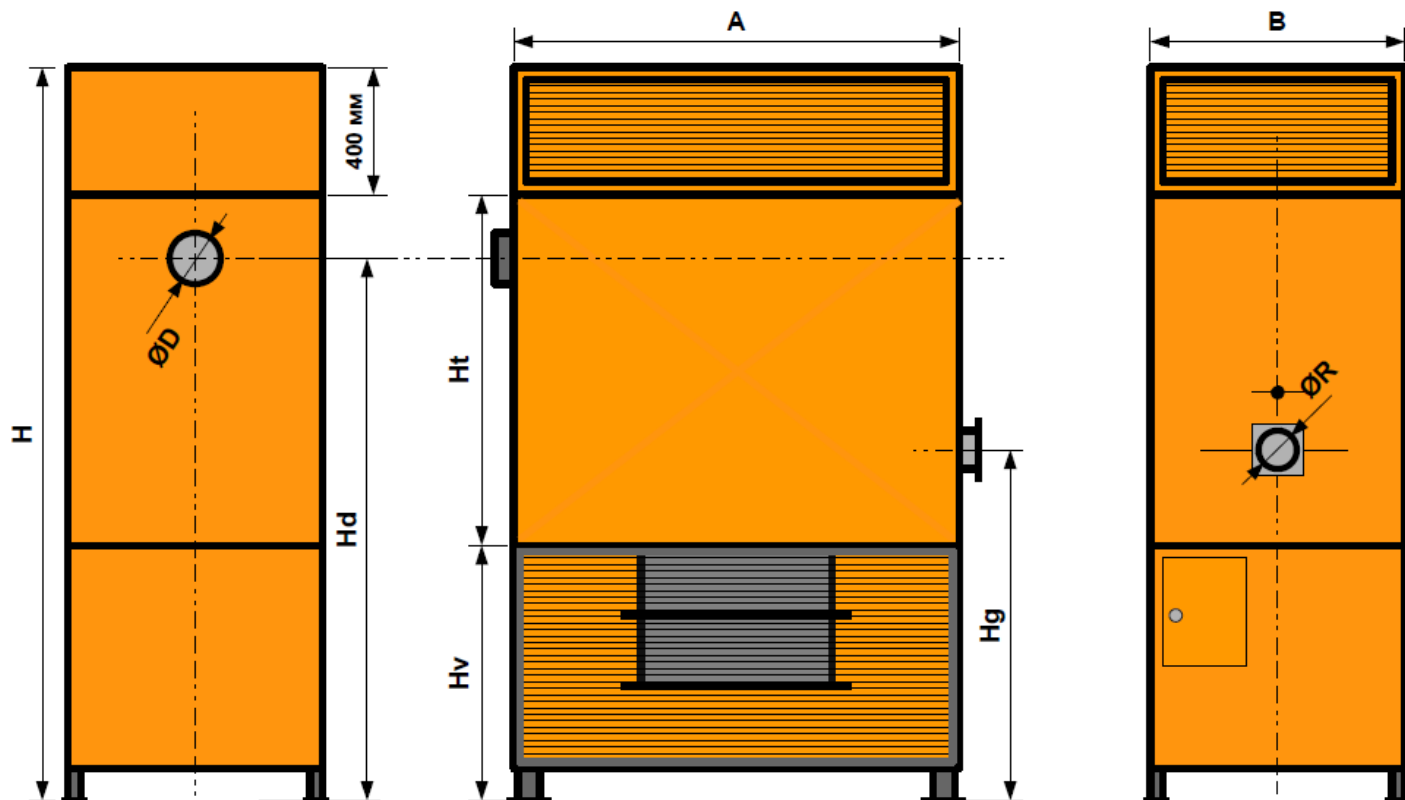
Габаритные размеры воздухонагревателей (теплообменников) серии VT-P D – присоединение газохода; R – присоединение горелки
